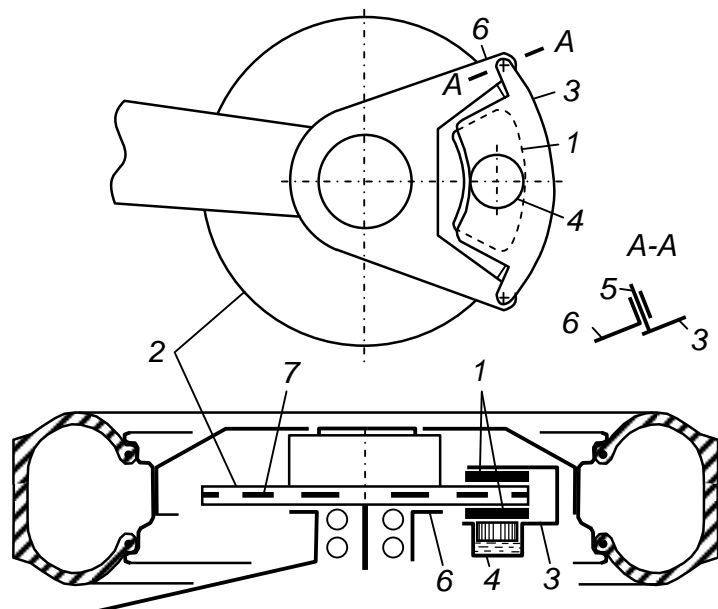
Схема колодочно-дискового тормозного механизма:
